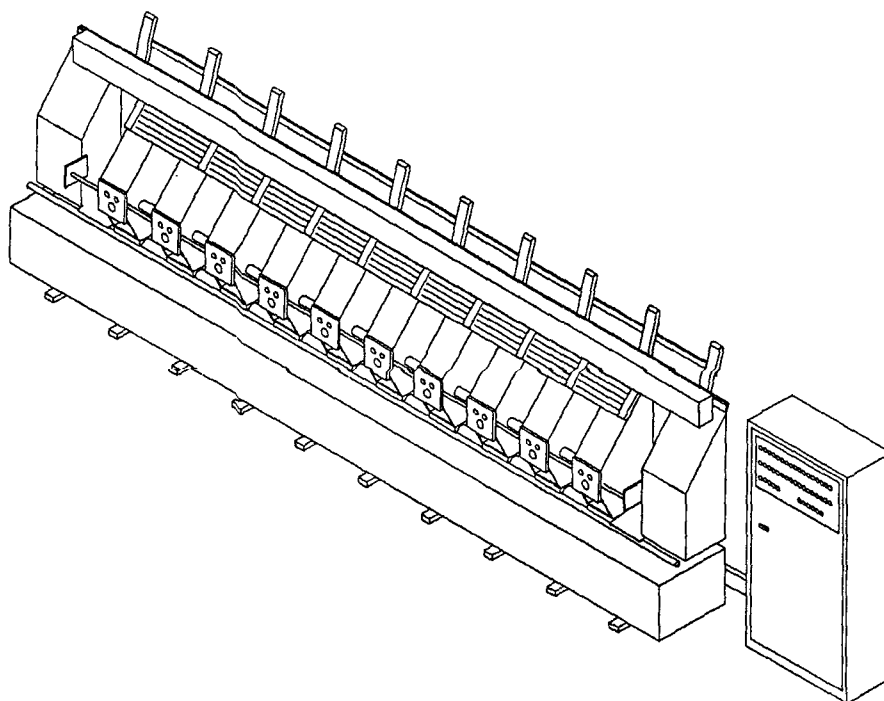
Круглопилний верстат з багатьма головками для фронтального розпилювання.
